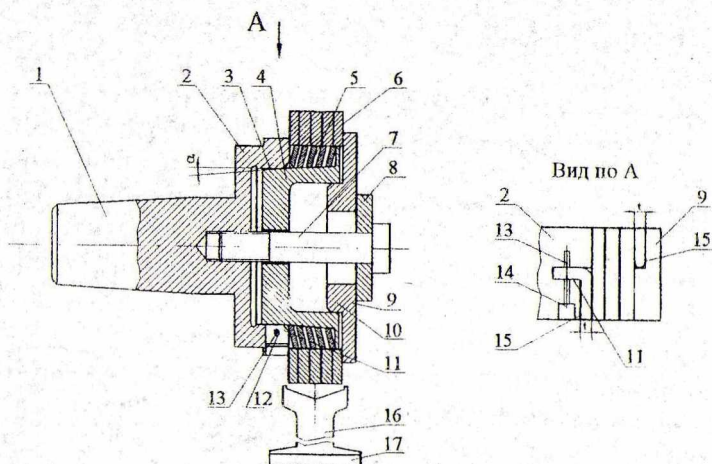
Оправка для профілювання і проточування гвинтових заготовок.
